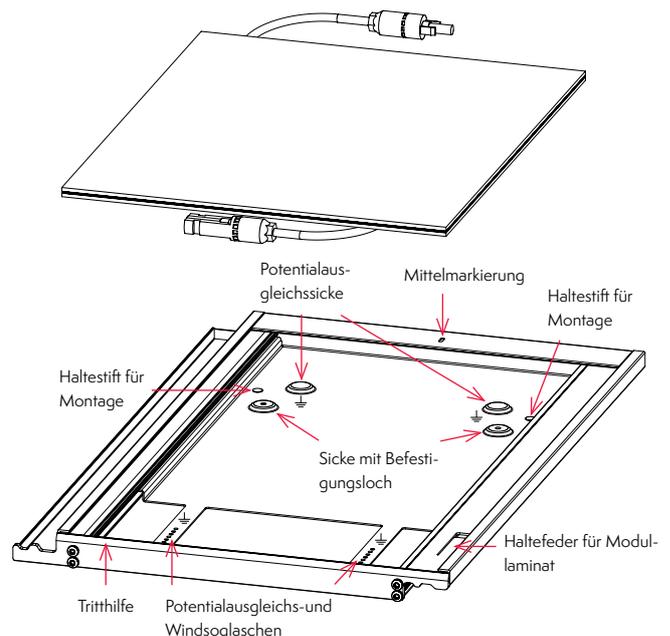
Bewegliches Modul-Laminat mit HJT-Zellstrings, J-Box mit PV-Kabeln inkl. Steckern (Bild oben), Solardachziegelgehäuse bestehend aus pulverbeschichteten stranggepressten Profilen und Blechen (Bild unten)
